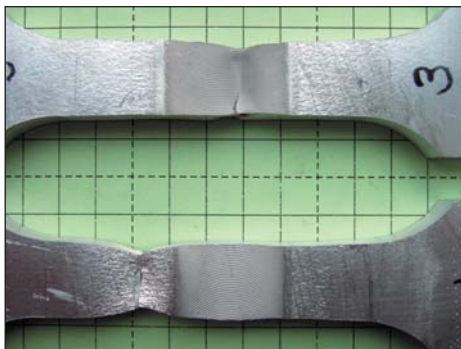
Результат испытания образца сварного шва из сплава АД0 на статическое растяжение
